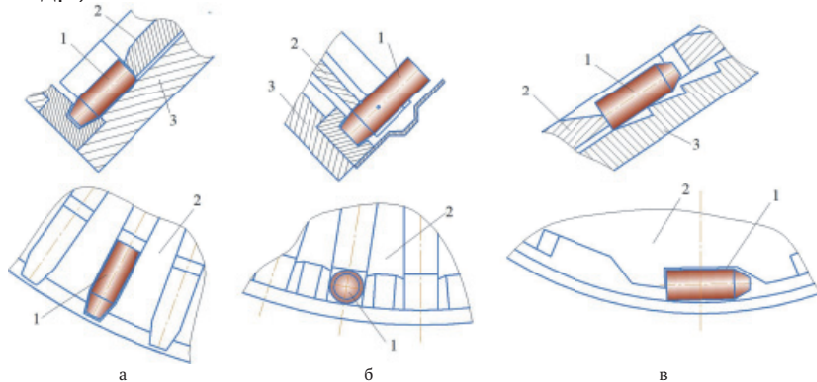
Схемы захвата заготовок захватывающими органами БЗУ:
